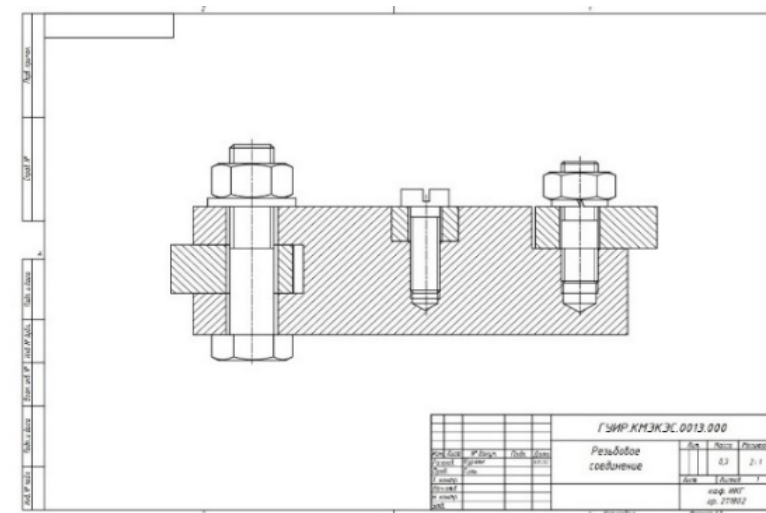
Автоматизированный 2D-чертеж сборочного узла резьбовых соединений
